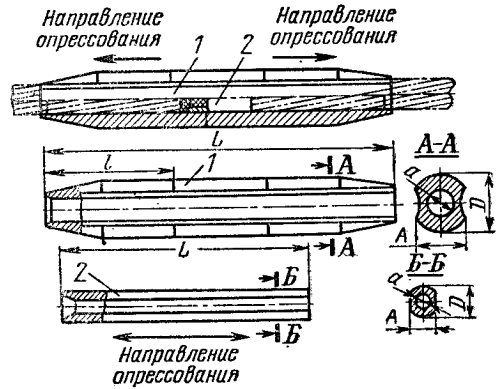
Соединительный прессуемый зажим типа САС для сталеалюминевых проводов, 1 — корпус; 2 — сердечник.
